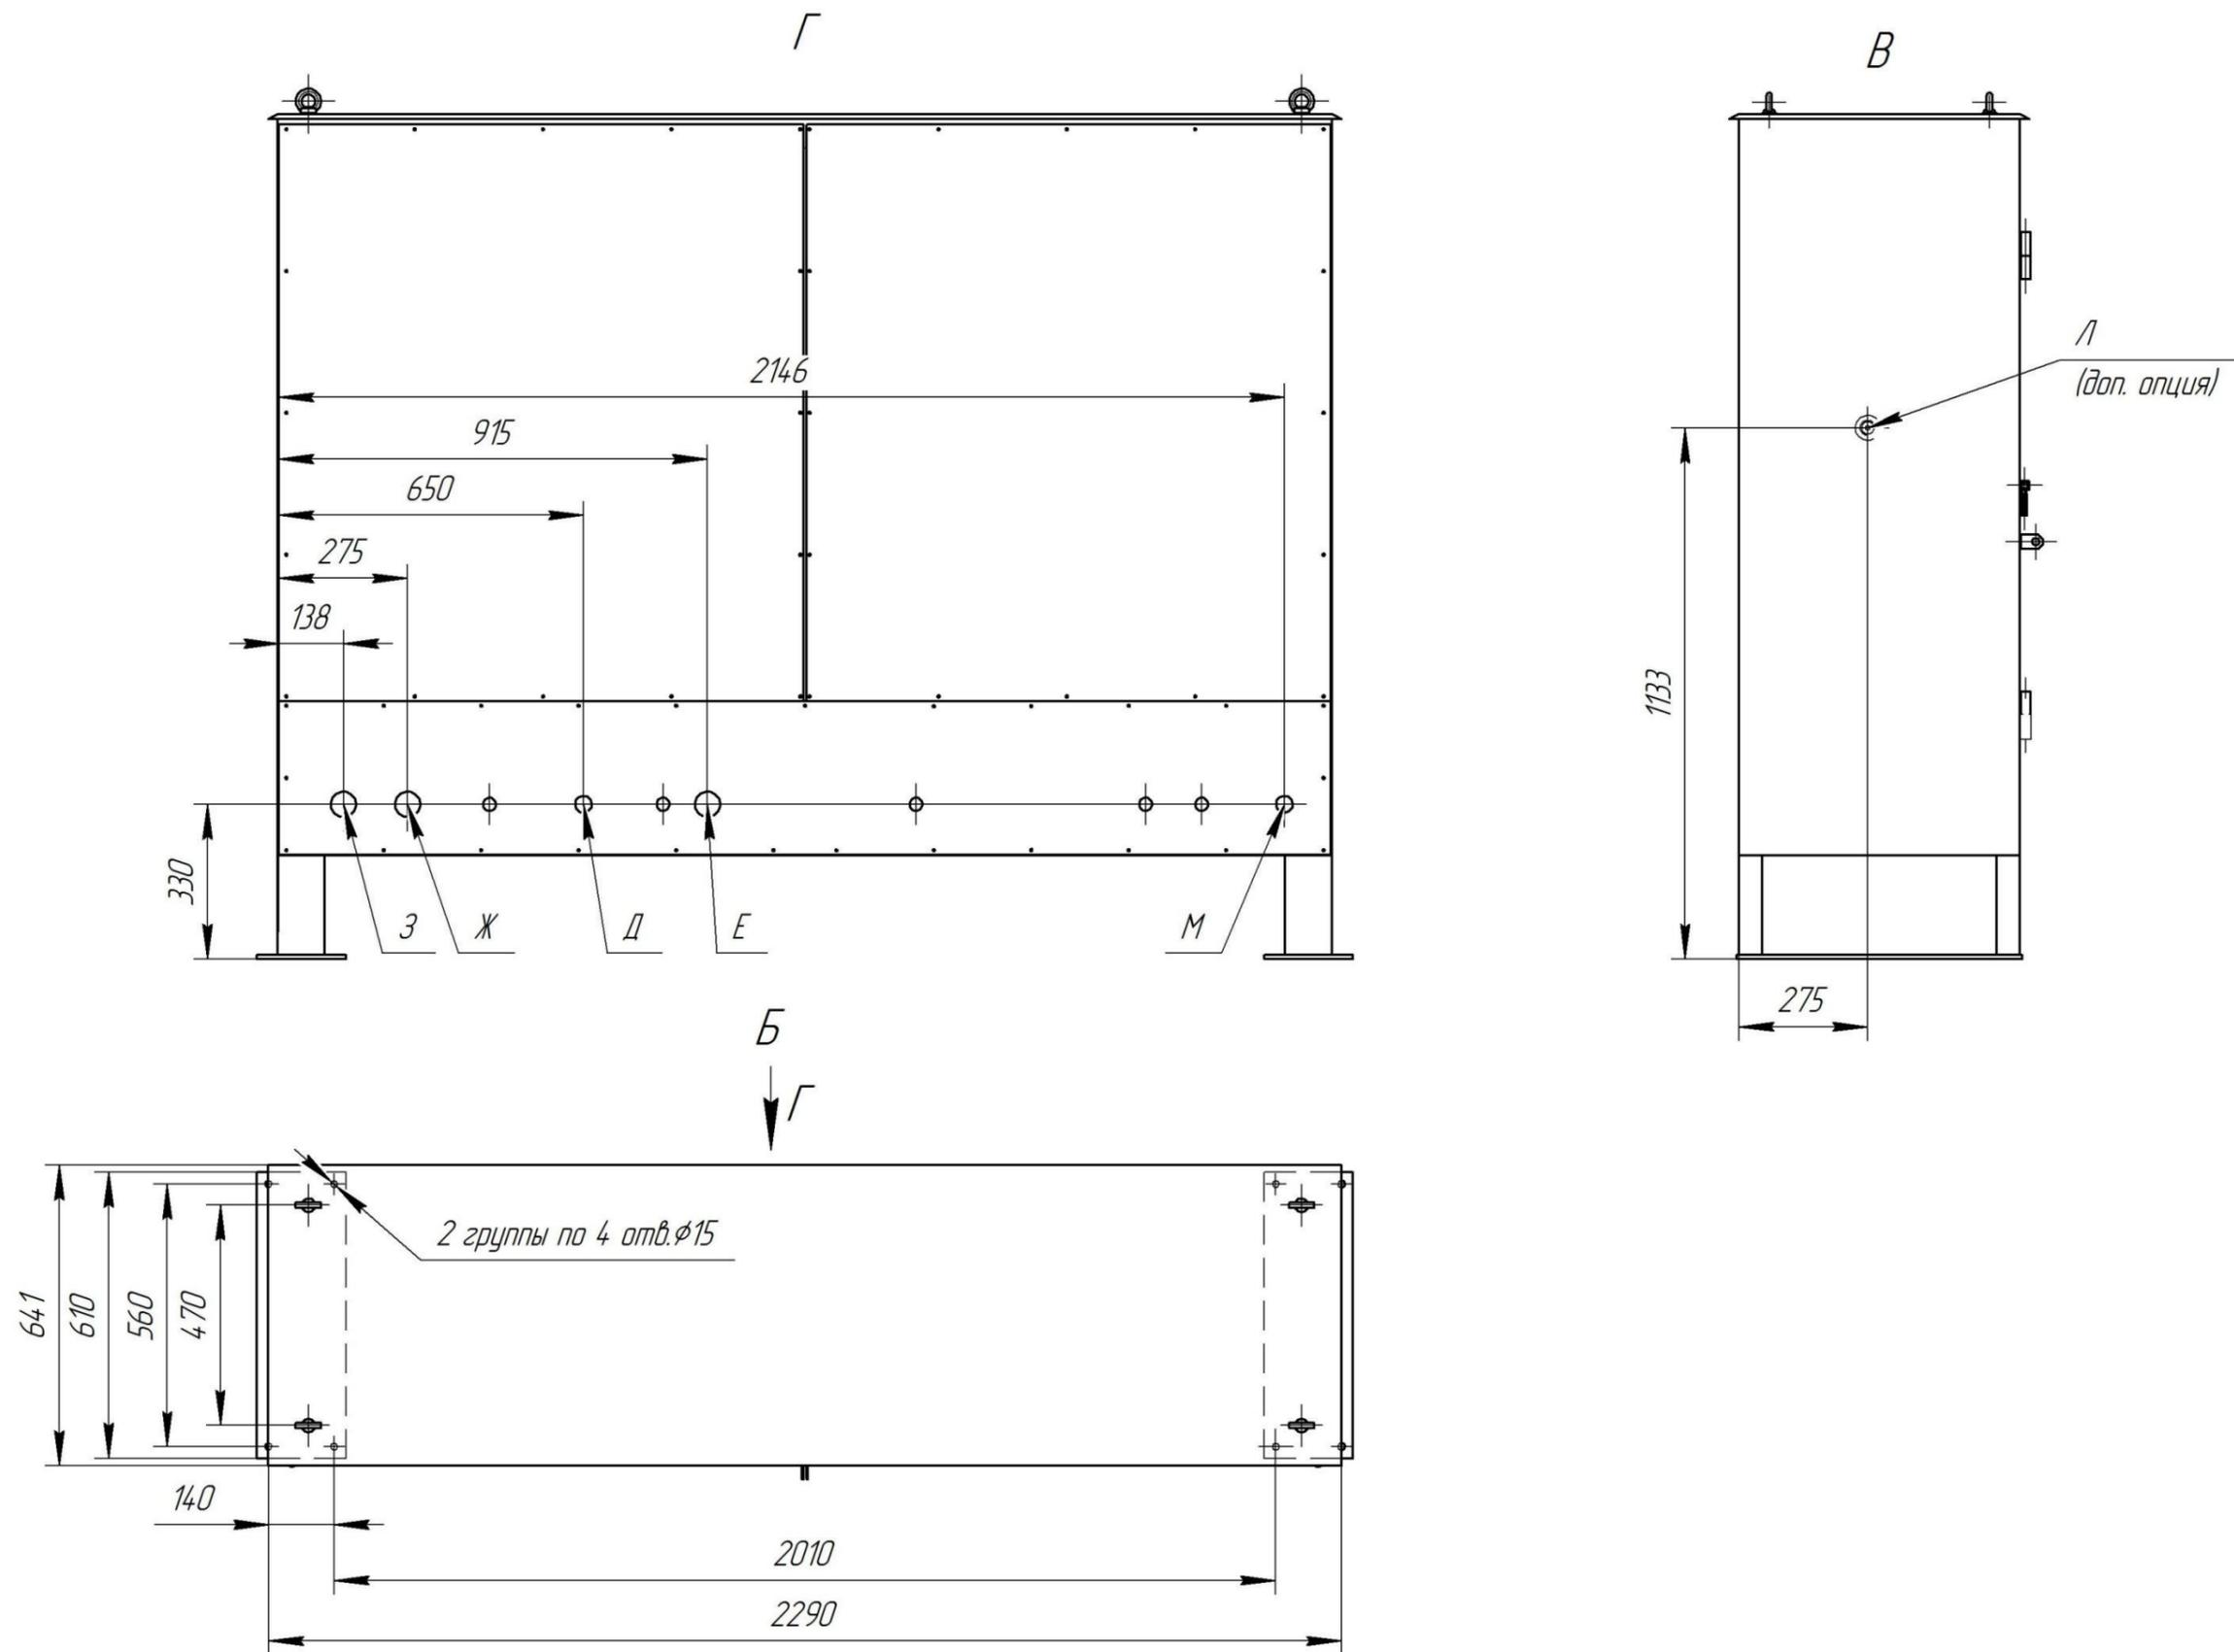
(лист 2 из 2) – Габаритные и присоединительные размеры БРХО
